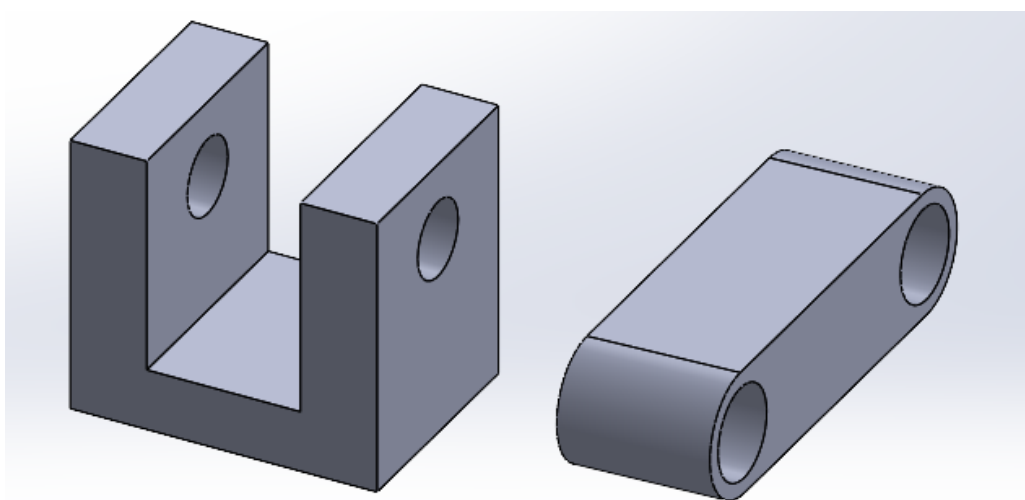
Деталі для з'єднання пневмоциліндра та воріт
